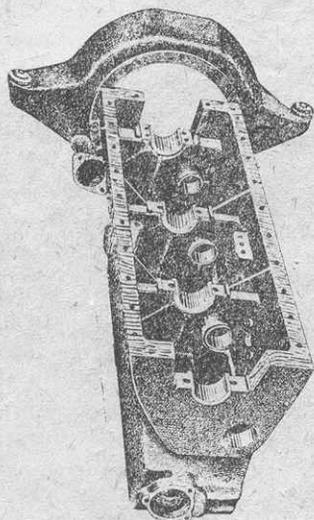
Вид блока цилиндров, изображенного на рис. 32, снизу.
